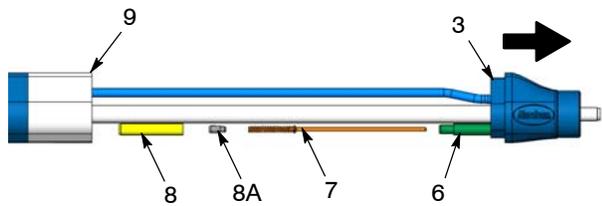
Smontaggio del resistore – Pistole con montaggio su barra
